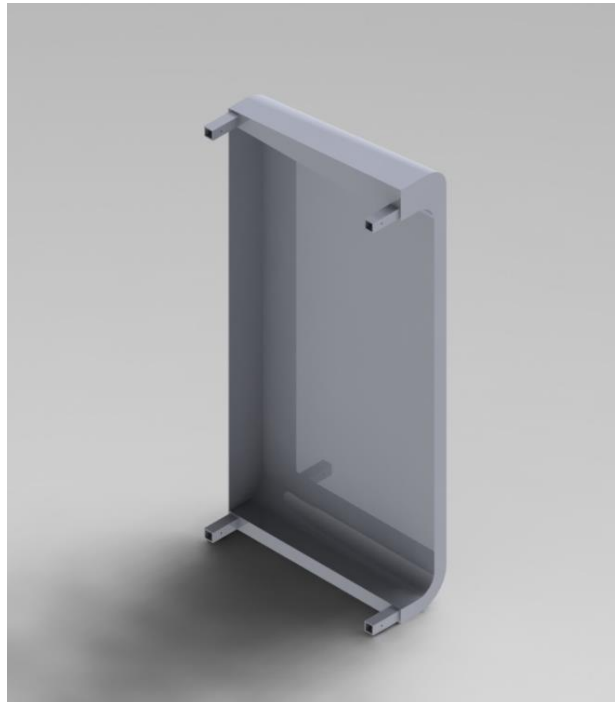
Ensamblaje subconjunto 1.2. Soldadura 15, 16, 17 y 18.
